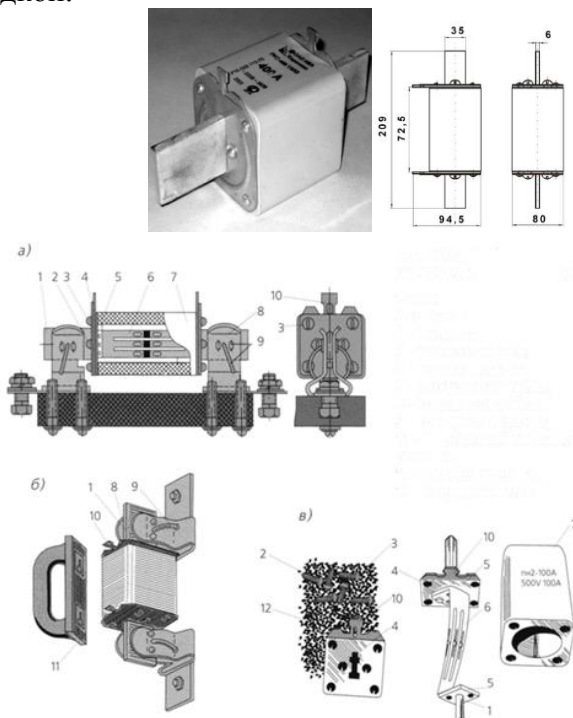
Предохранитель ПН-2: 1- нож; 2, 3 – винты;
